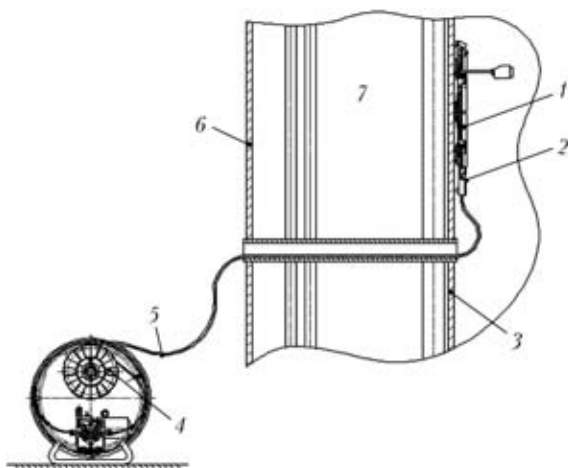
Схема сварки на внутренней стенке биологического защитного экрана: 1 — ремонтный робот; 2 — приспособление для равномерной подачи проволоки; 3, 6 — соответственно внутренняя и внешняя стальная стенка; 4 — механизм подачи проволоки; 5 — канал для подачи проволоки; 7 — биологическая защита из бетона
